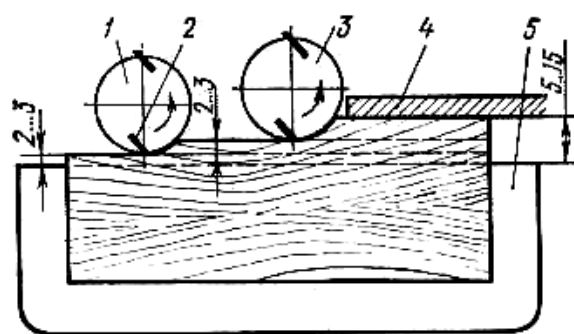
Настройка ножевых головок кромкофуговального станка: 1 — ножевая головка для окончательного фрезерования, 2 — нож, 3 — ножевая головка для предварительного фрезерования, 4 — упорная линейка, 5 — стол станка
